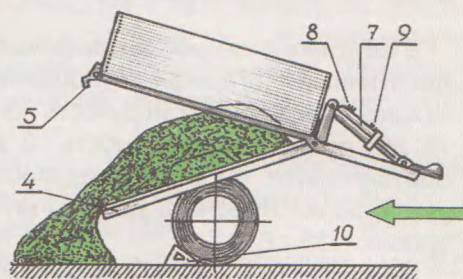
4 — днище кузова; 7 — пневмоцилиндр; 8 и 9 — ниппели; 10 — колodka.
